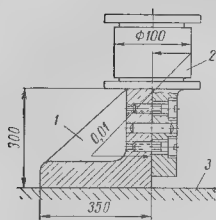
Центровка специального приспособления для расточки корпусов турбины на карусельном станке:
